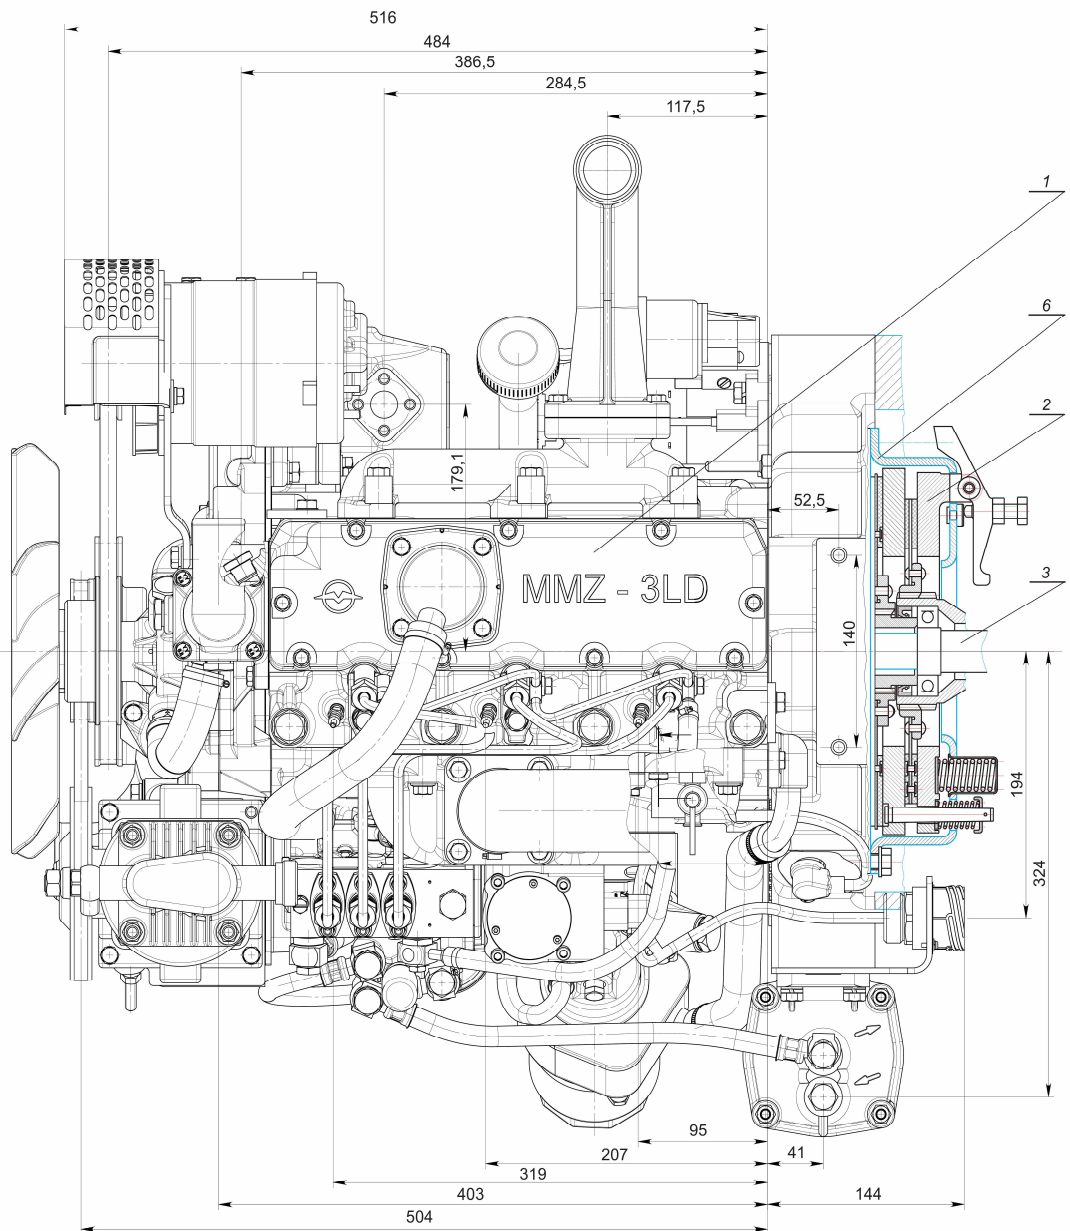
Загальний вид двигуна MMZ-3LD у зборі з дводисковим зчепленням (вид зверху)
